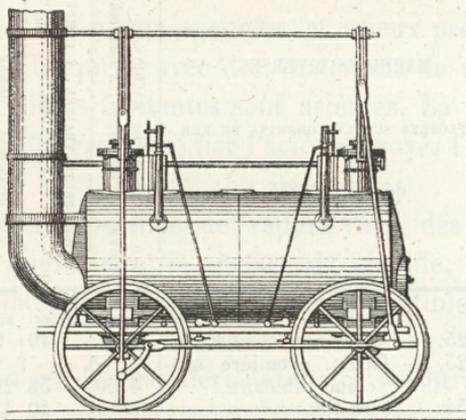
Machine à bielle d'accouplement de Stephenson.
